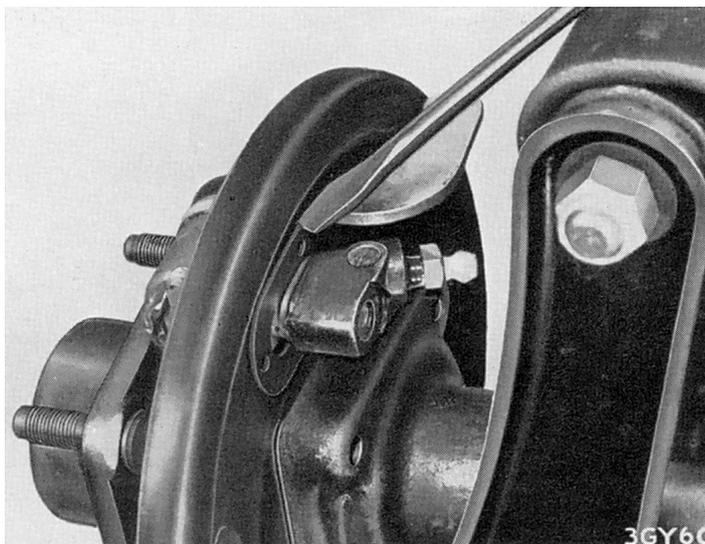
Dépose de la plaque de fixation du cylindre de frein arrière
